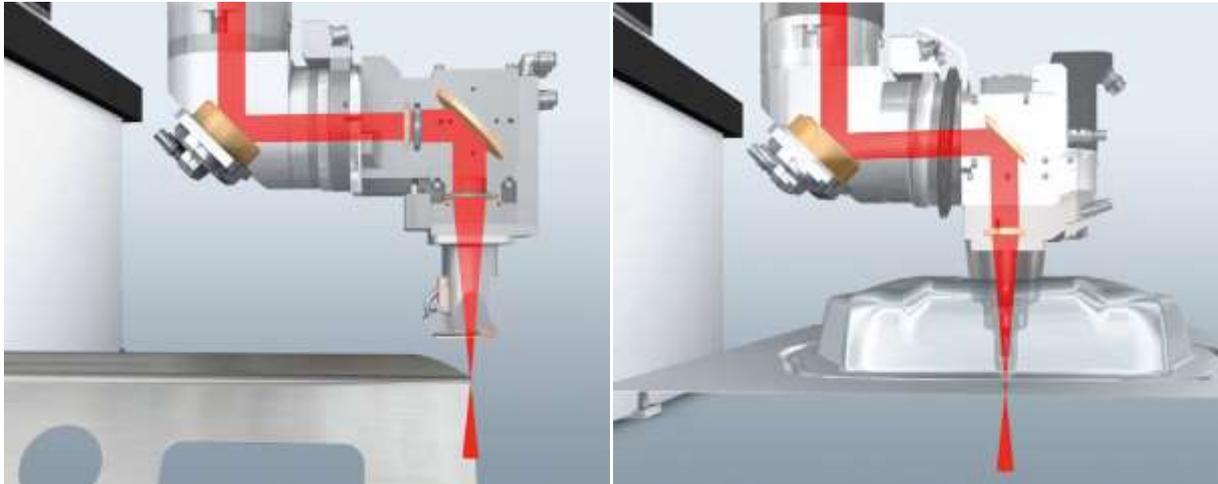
Technologie Schweißen (Links) und Schneiden (Rechts) (Quelle: /51/)
